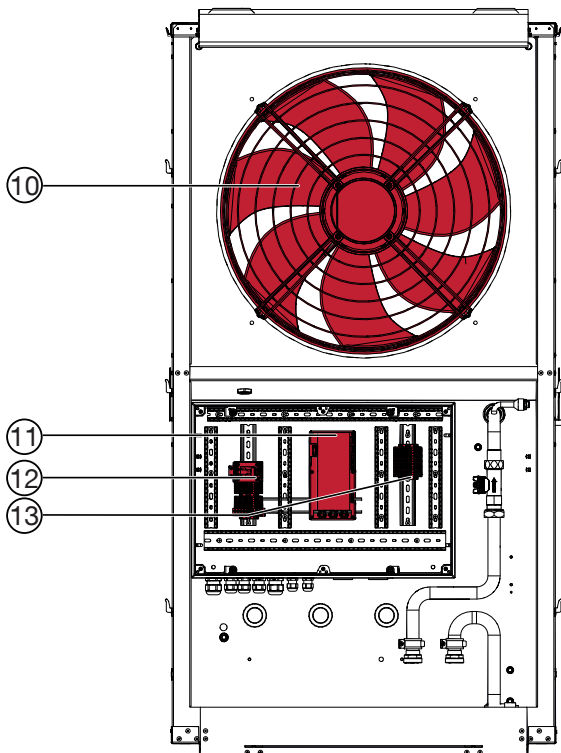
WP - Rückansicht geöffnet (Symbolbild)
